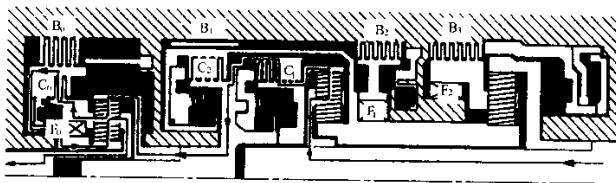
2 档齿轮 (换挡杆置 2 或 L 位置)、发动机制动结构简图
